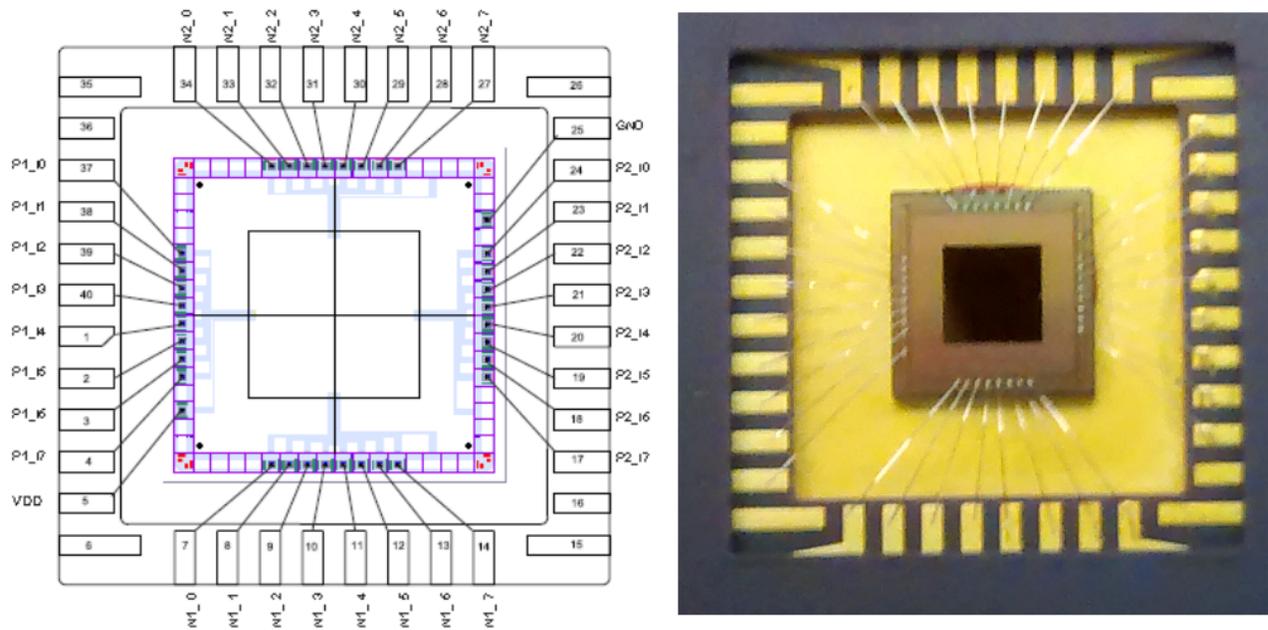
Diagrama de Solda (*wiremap*) do *Chip* sensor piezo-transdutor no empacotamento DIP-40 e foto do dispositivo encapsulado.
